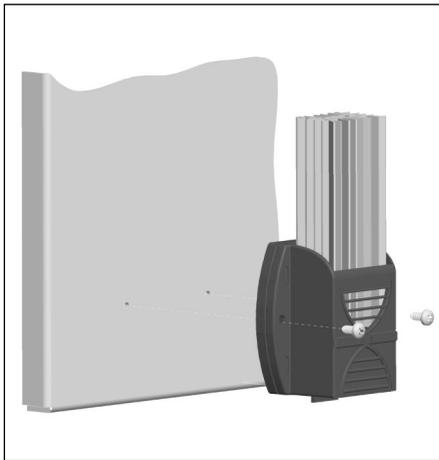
Schraubbefestigung auf einer Montageplatte
